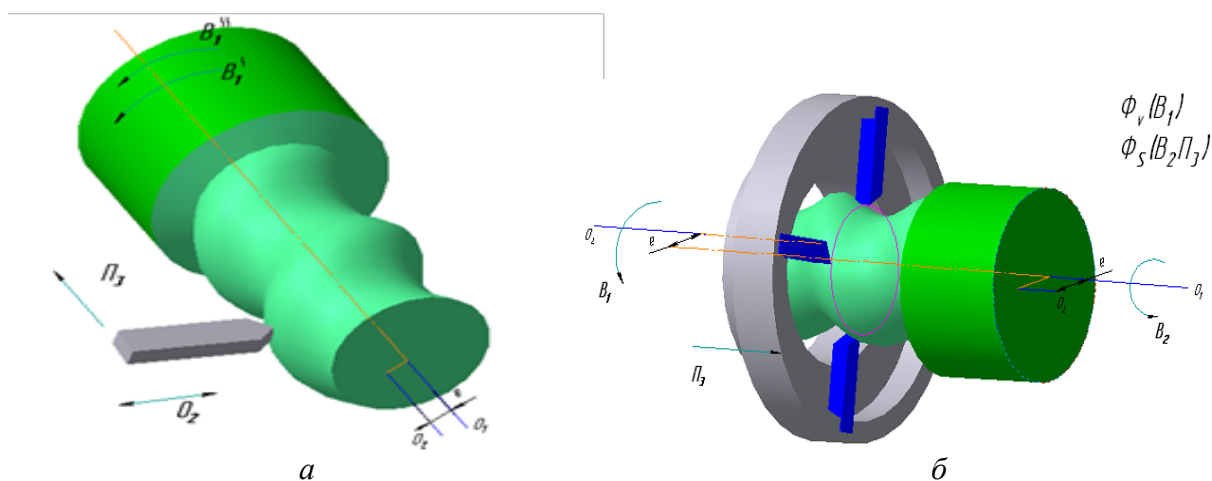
Кинематические схемы обработки круговых винтовых поверхностей на токарно-затыловочном станке
